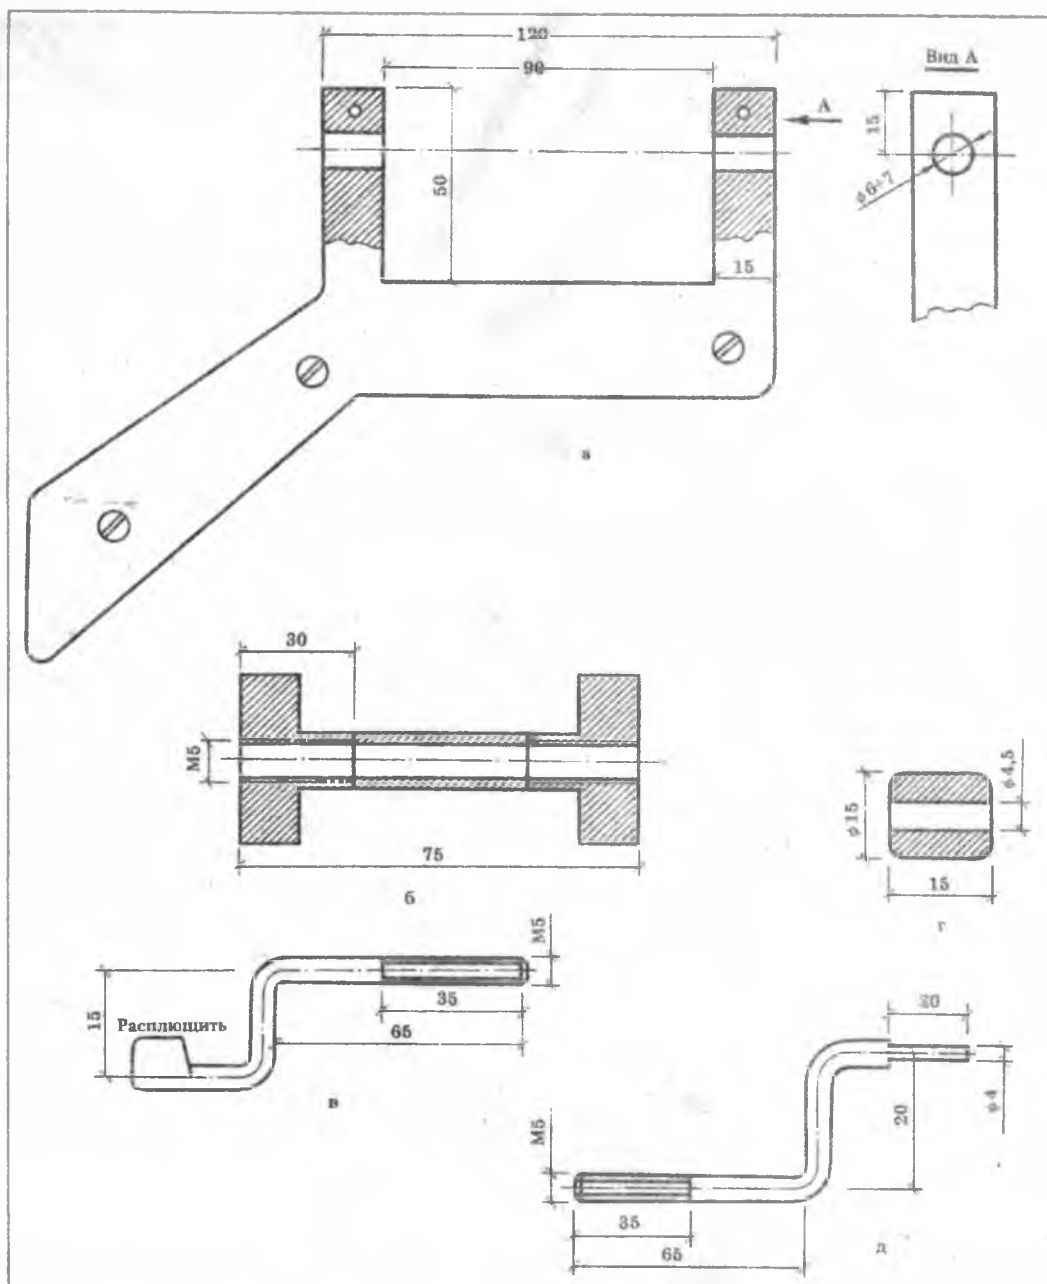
Детали моталки: а — корпус; б — катушка; в — рука с расплюснутым концом; г — бо-
